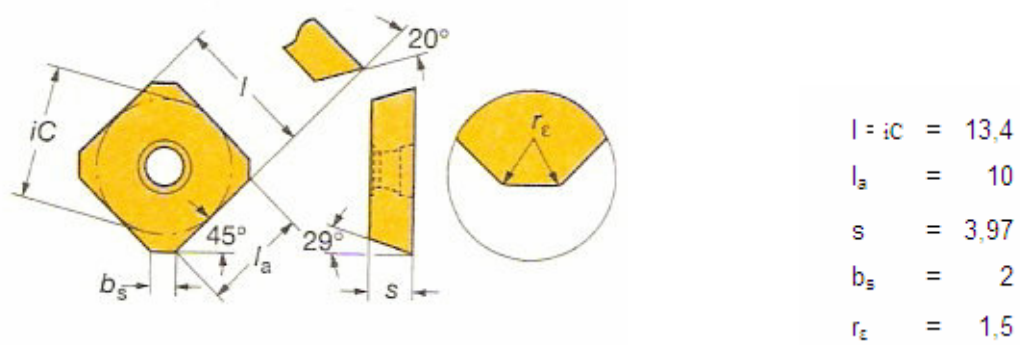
Dimensões da ferramenta de corte (SANDVIK, 2006)
